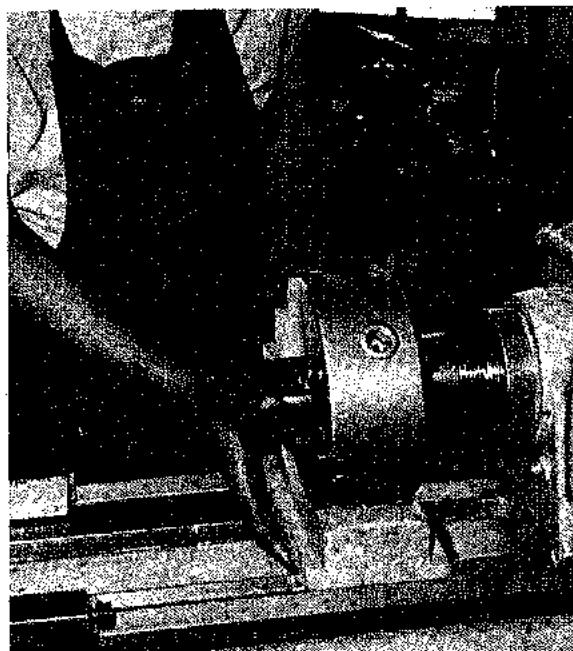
Montaje del plato con el auxilio de un bloque de madera especialmente diseñado.
